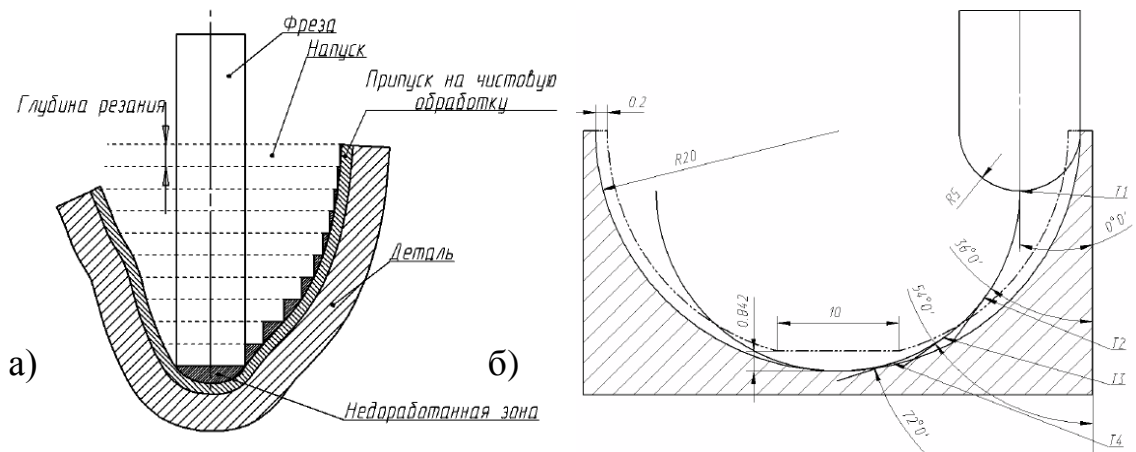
Схема послойного черного снятия припуска, схема обработки криволинейной поверхности концевой сферической фрезой [68]
